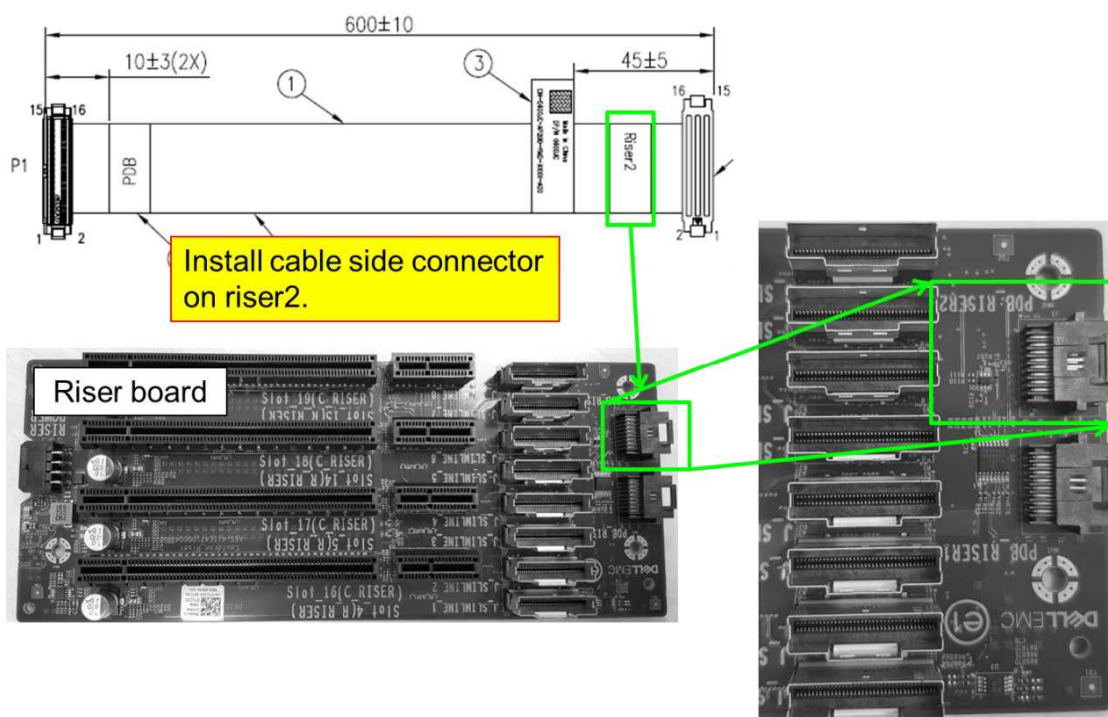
Assemblage du câble IDC (carte de montage 2-PDB) vers carte de montage 2
